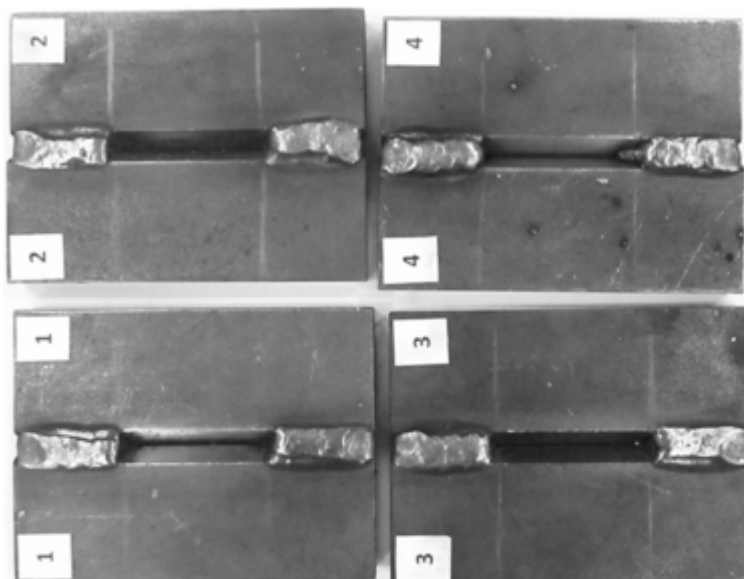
Фотографии проб «Тэккен», собранных под сварку испытуемого сварного шва
